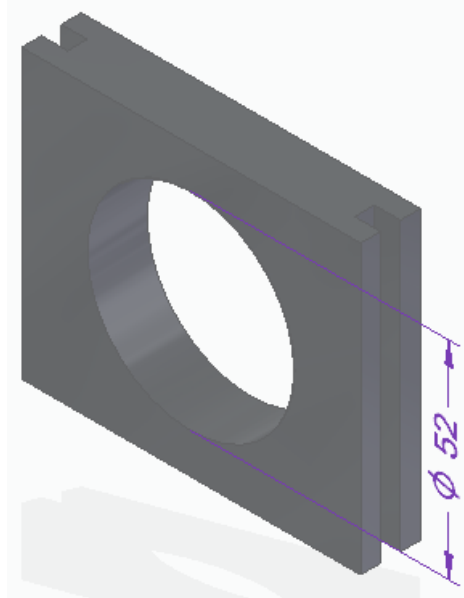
Ensamblaje de los soportes de los rodillos de acoplamiento
